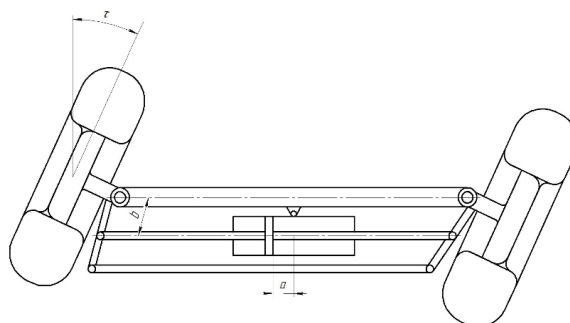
Кинематическая схема поворота передних управляемых колес
